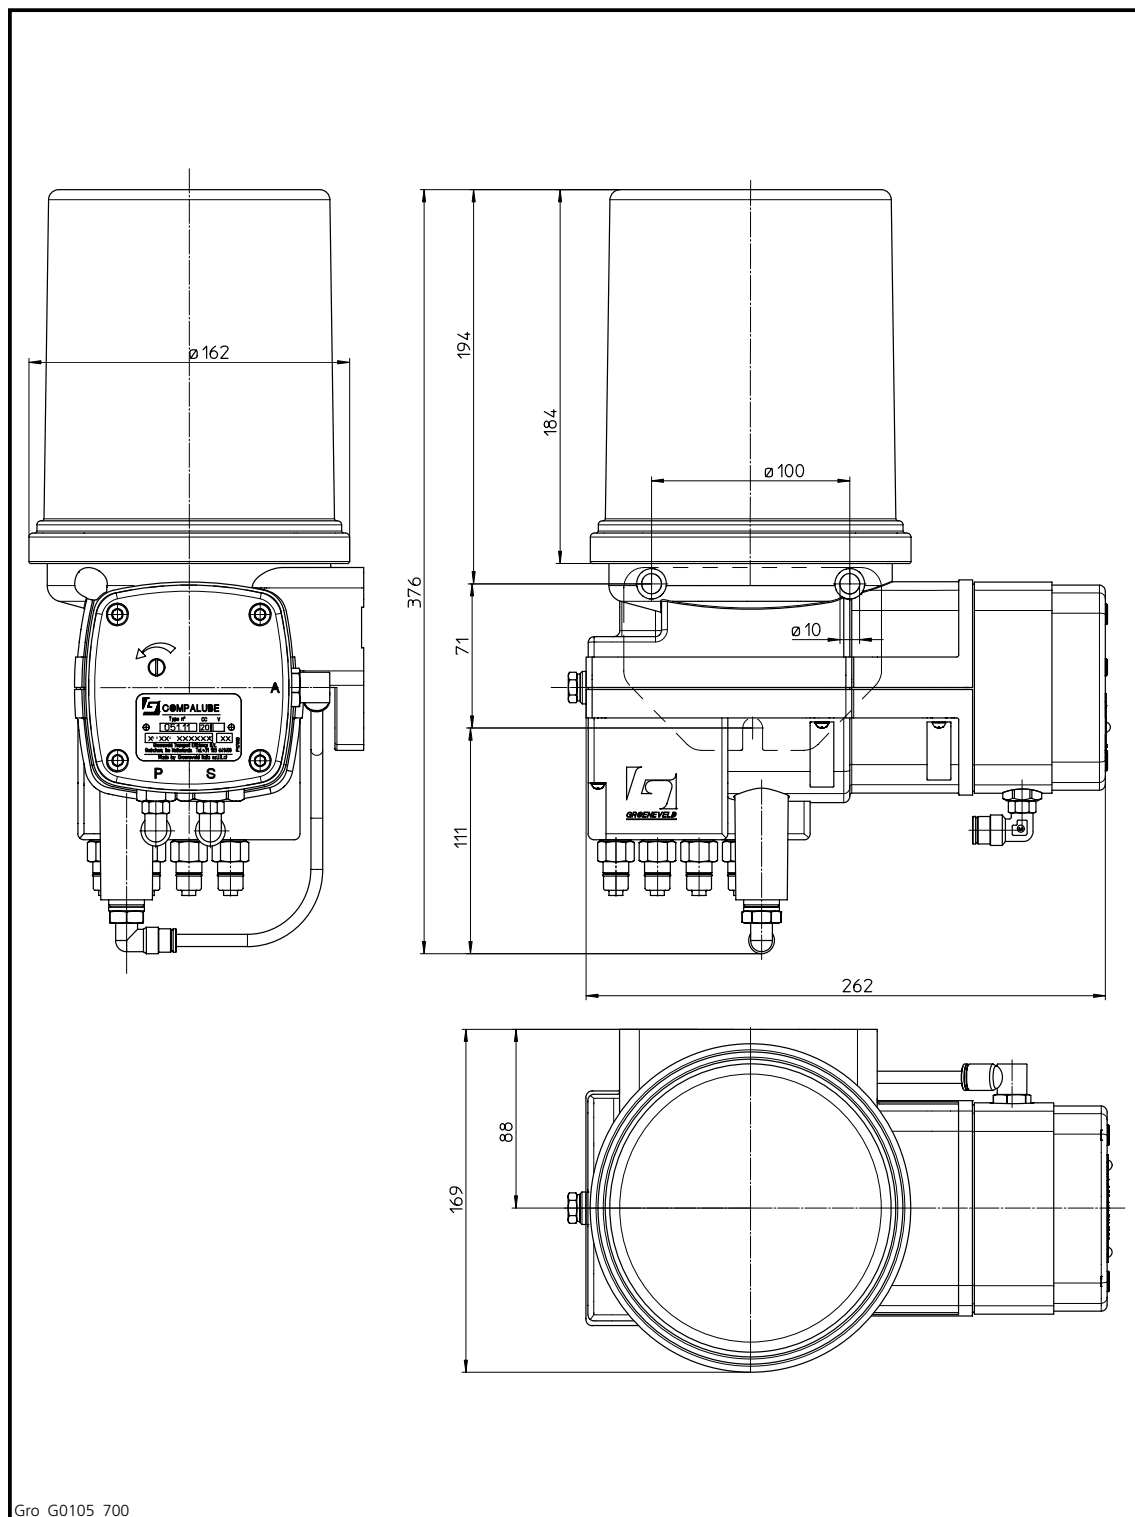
Dimensioni del gruppo pompa CompAlube
